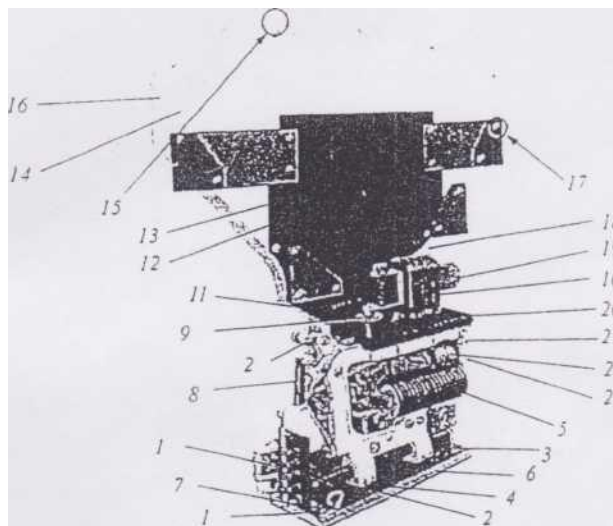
Быстродействующий выключатель БВП-3
